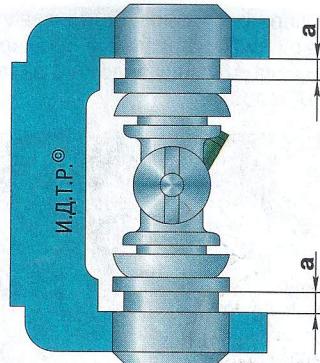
Схема запрессовки подшипников карданного шарнира
